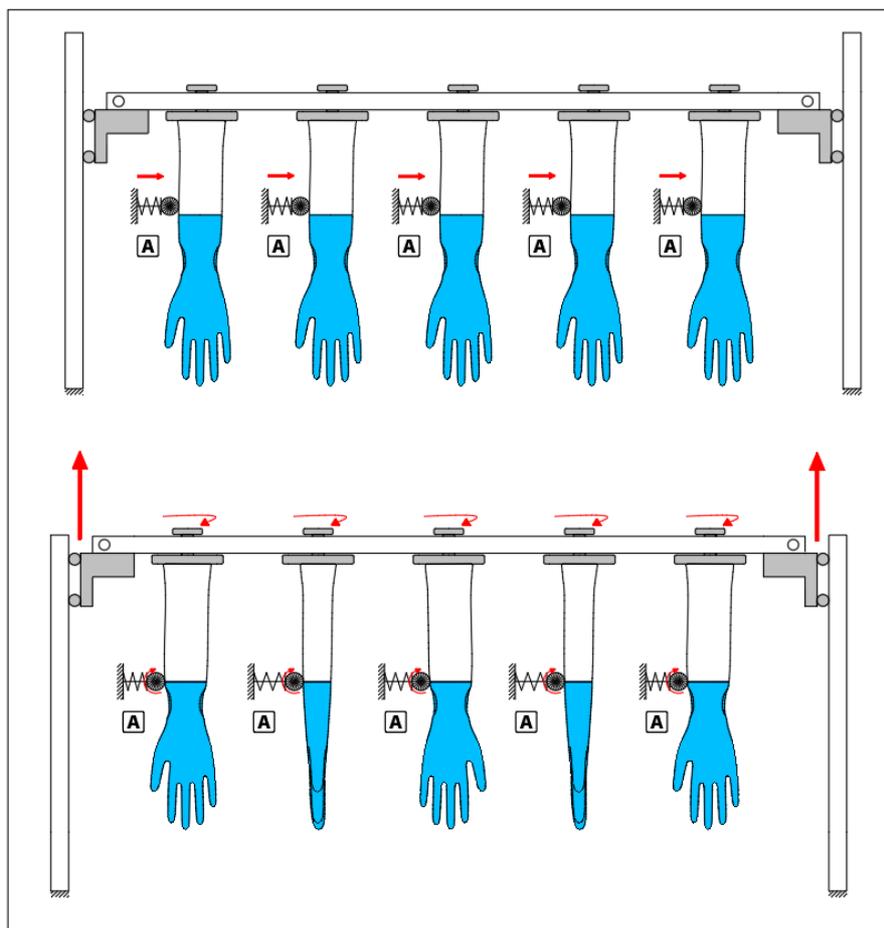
Ilustração do processo de beading para sistema automático em lote.
